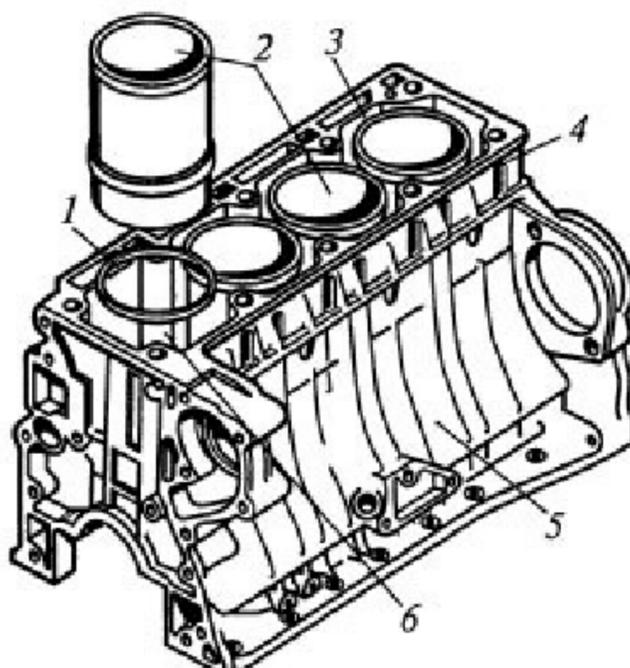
2. Блок двигателя со съёмными гильзами цилиндров:
